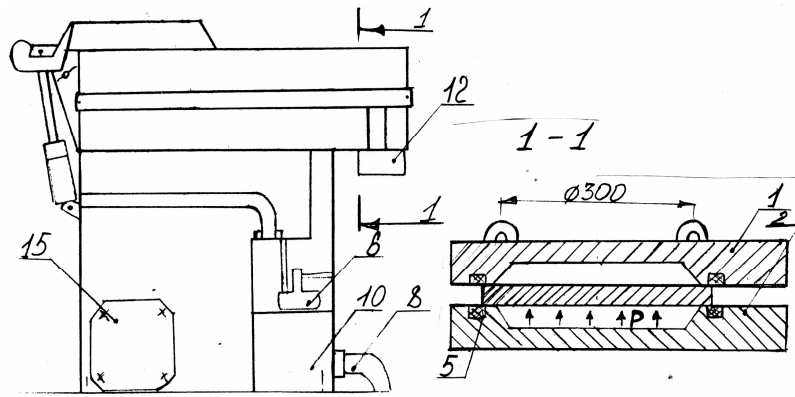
Установка для испытания в условиях двухосного изгиба сварного образца
